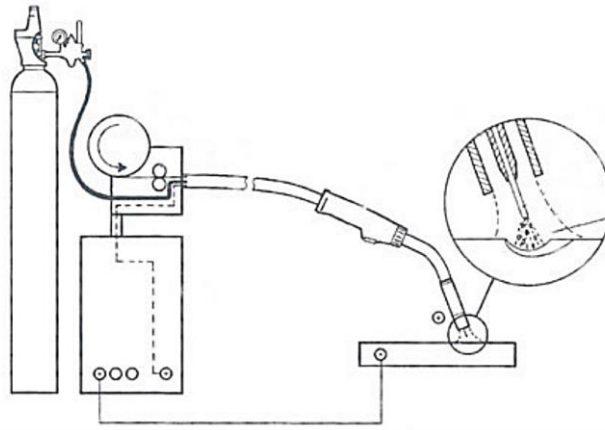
Esquema de soldadura MIG (DMYH, 2011).
